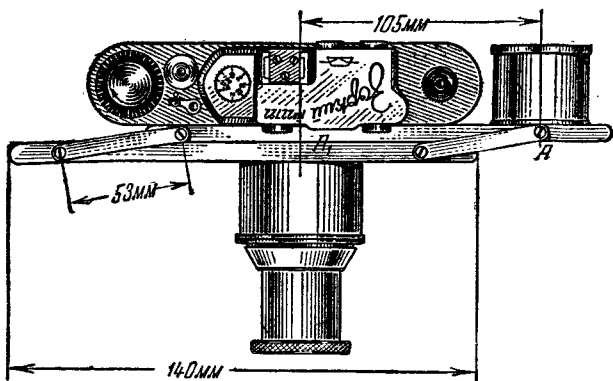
Устройство для наводки по матовому стеклу с перекидной планкой
